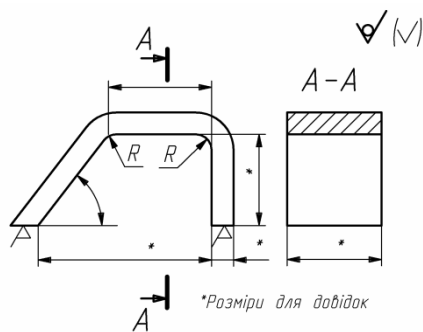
Кресленник скоби, виготовленої гнуттям
